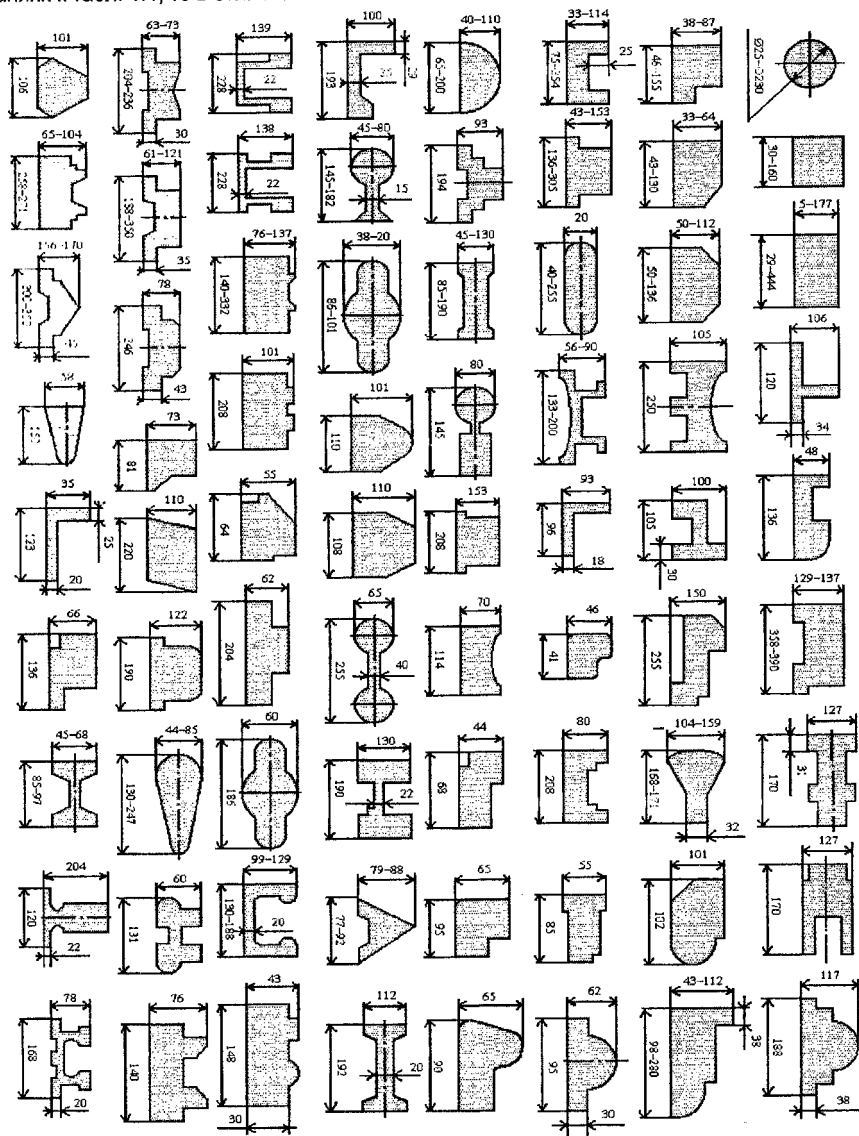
Профили заготовок, получаемых методом ГНД
